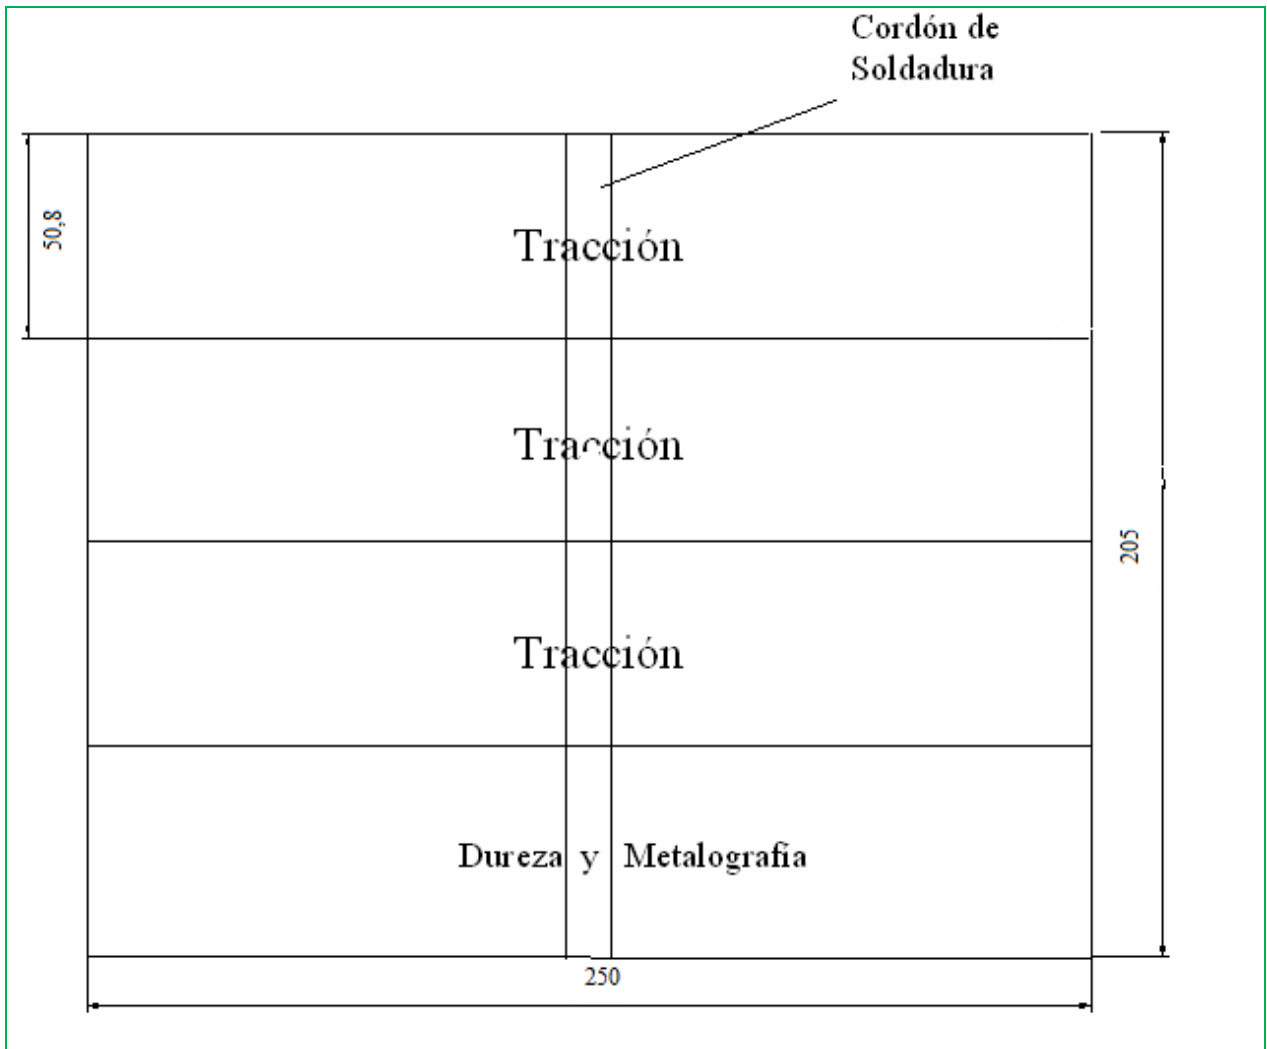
Esquema de la distribución del material soldado, láminas de 205x250, dimensiones en mm.
